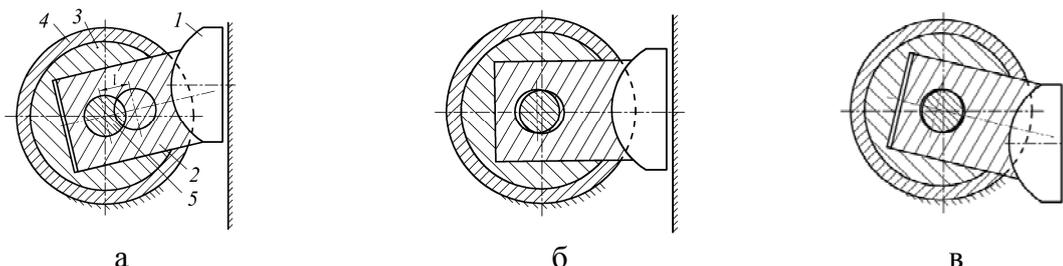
Схема устройства для резки проката, содержащего группу Ассура третьего вида: а – положение I; б – положение II; в – положение III
